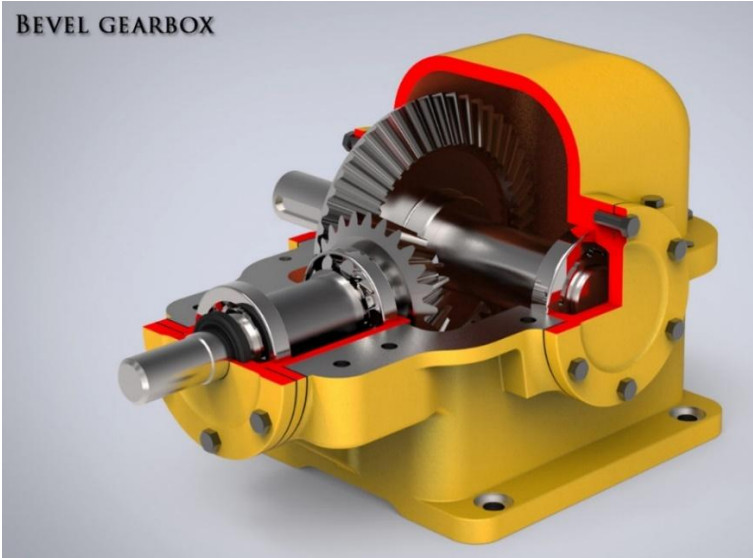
Редуктор одноступінчастий конічний, загальний вигляд [59]
